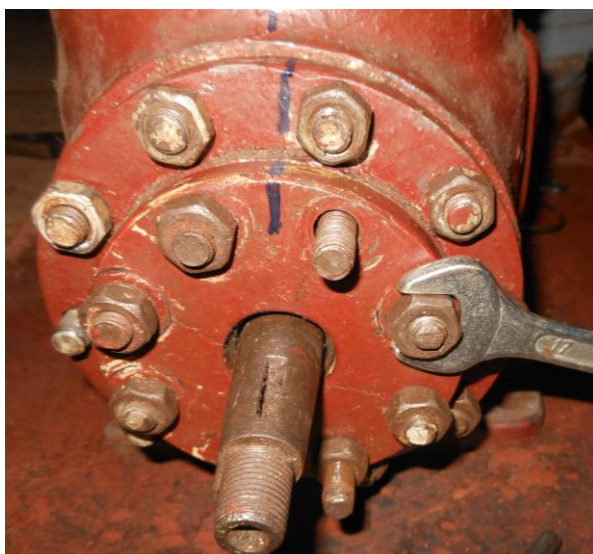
Ослабление затяжки гаек крепления крышки уплотнения коленчатого вала к корпусу подшипника
